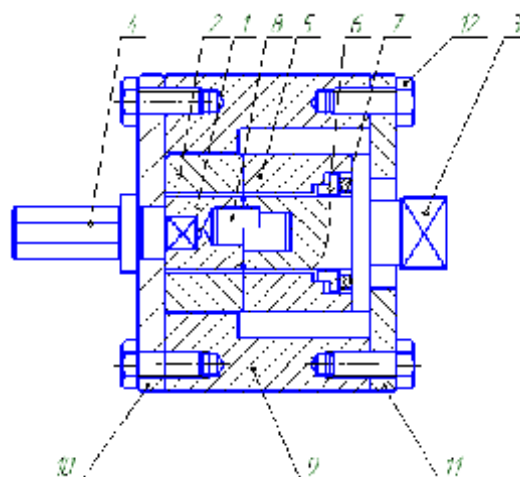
Конструкция устройства для резки труб сдвигом и кручением.
